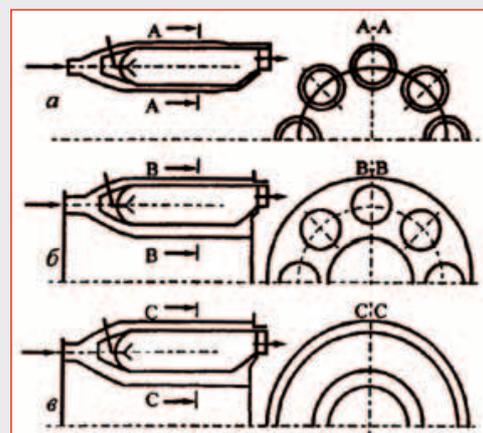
Конструктивные схемы камер сгорания: а - трубчатая; б - трубчато-кольцевая; в - кольцевая
